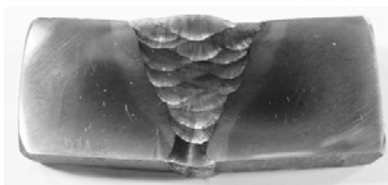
Загальний вигляд зварного з'єднання, положення 1G
